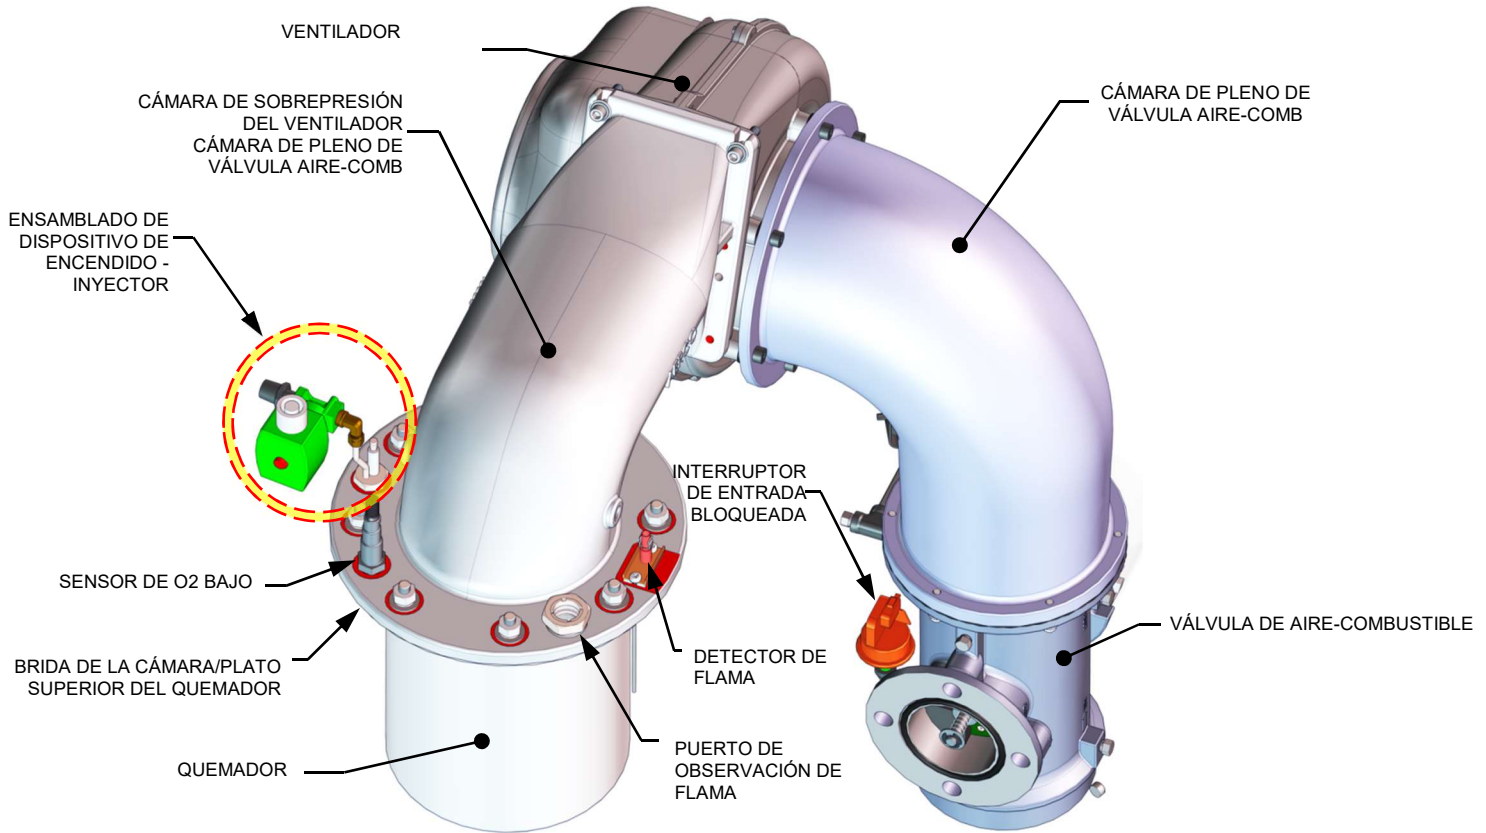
Ensamblado del quemador de BMK 1500/2000 (retirado de la caldera)
